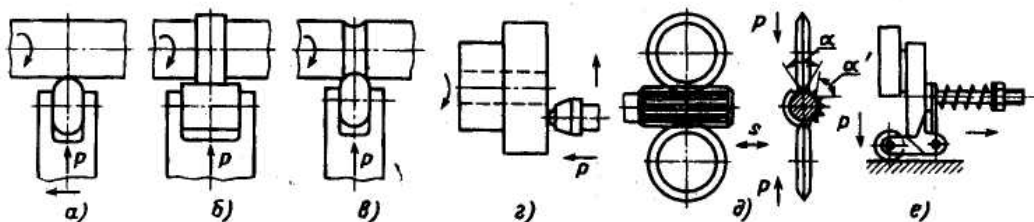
Схеми зміцнення деталей обкатуванням: а – роликом з повздовжньою подачею; б - роликом з поперечною подачею; в – фасонним роликом з поперечною подачею; г торцевої поверхні кулькою; д – роликами поверхонь шліців; е - плоскої поверхні роликами
